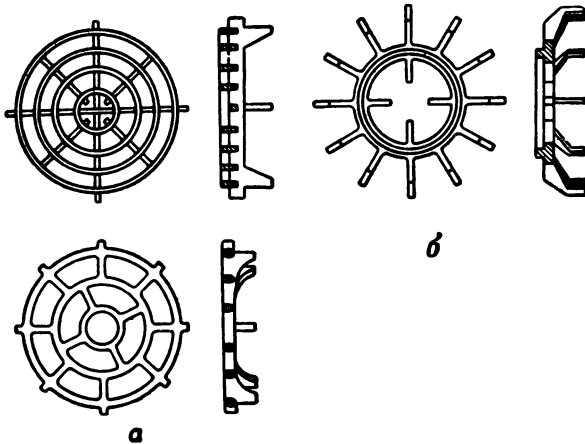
Конструктивные формы диафрагм для ракетных двигателей на твердом топливе:
